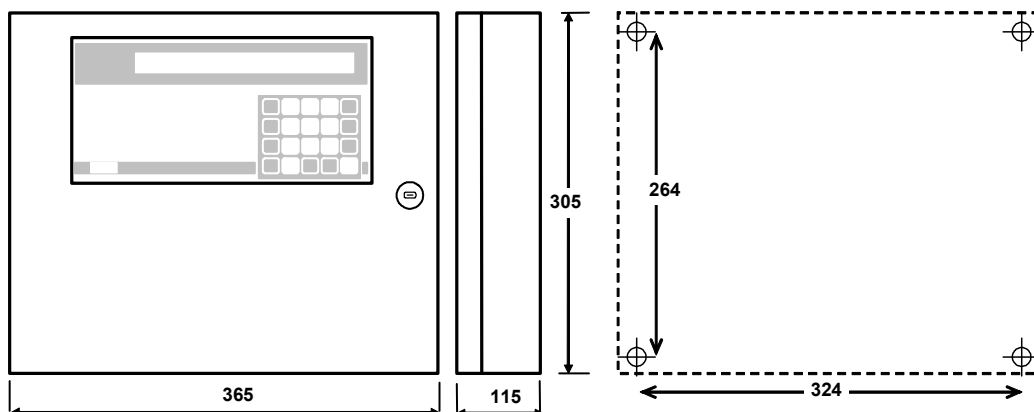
CE700P Dimensioni e Dima di fissaggio a parete
